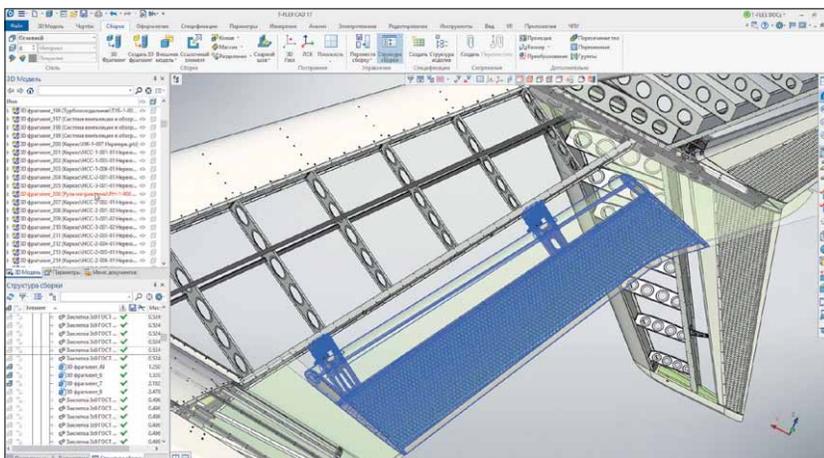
Модель композитного руля направления с сотовым наполнителем в контексте сборки хвоста в T-FLEX CAD
